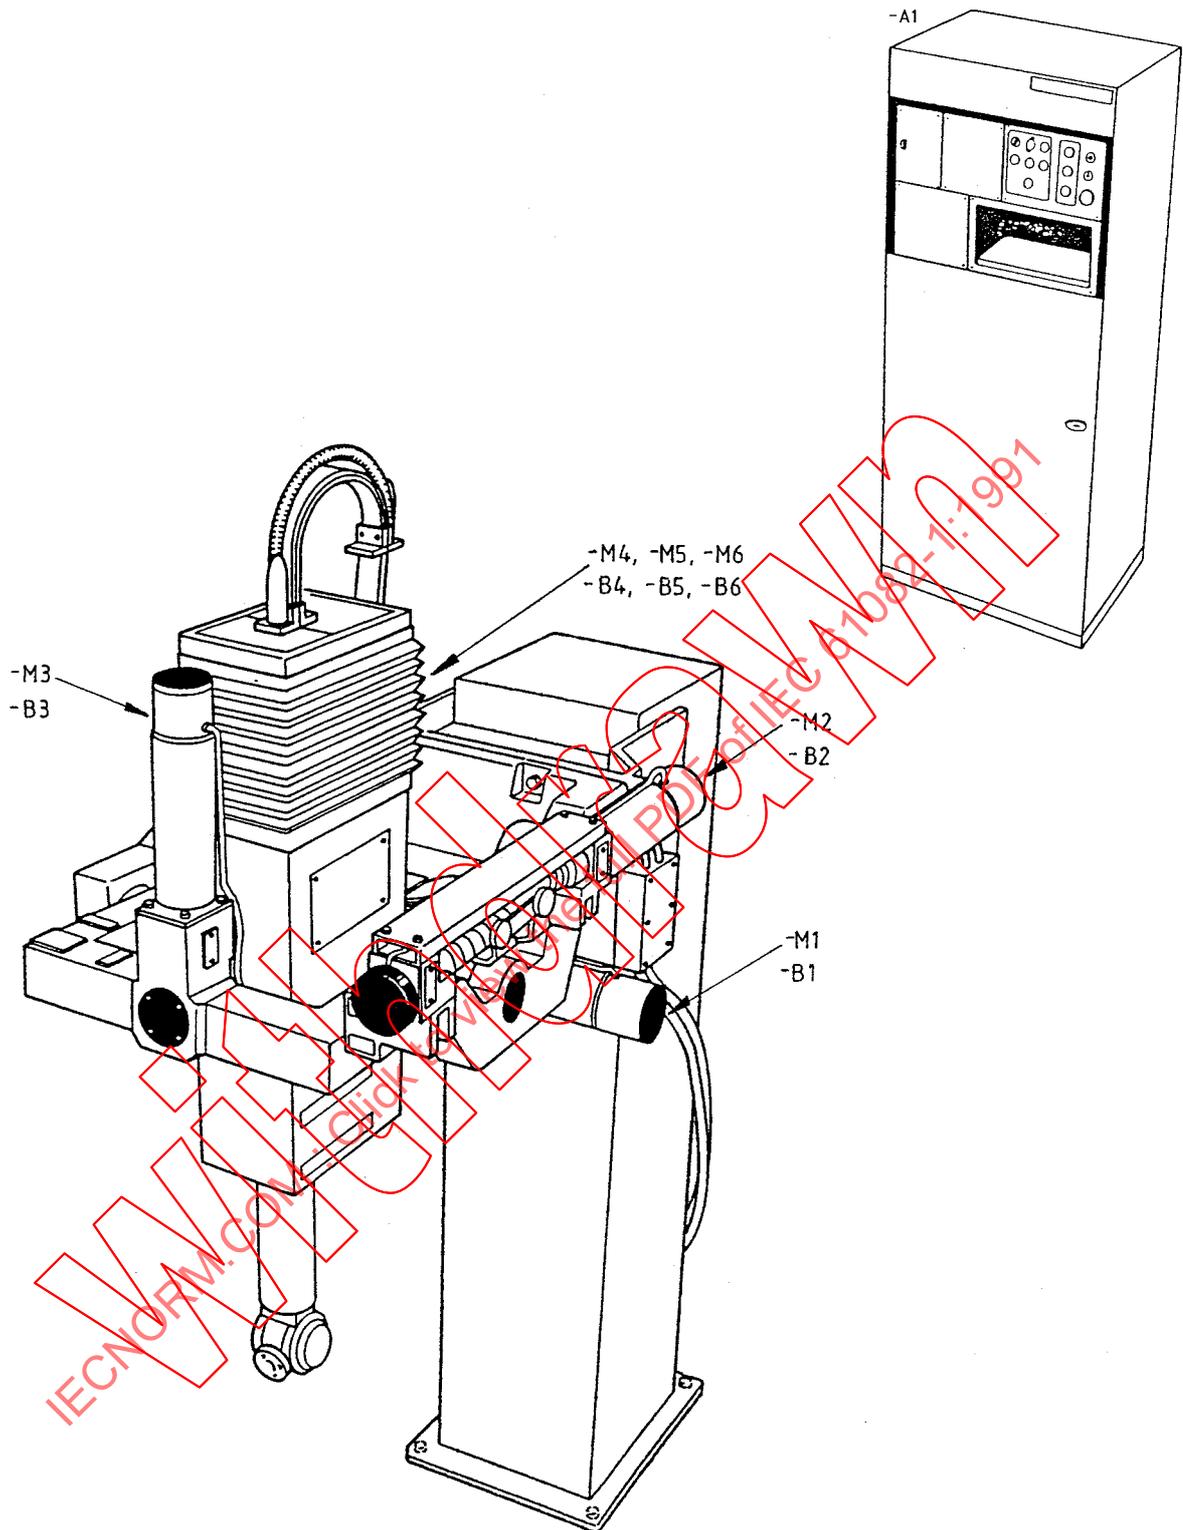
Exemple d'un dessin d'installation; robot électrique.
